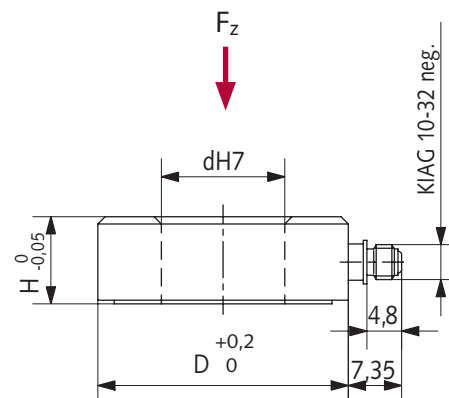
Dimensions rondelle de charge, Type 9041A ... 9071A
